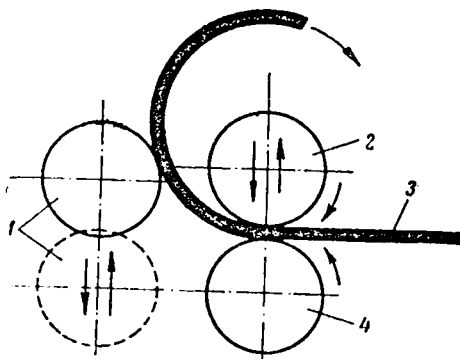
Схема получения гибкой детали цилиндрической формы на листогибочном трехвалковом станке по несимметричной схеме
